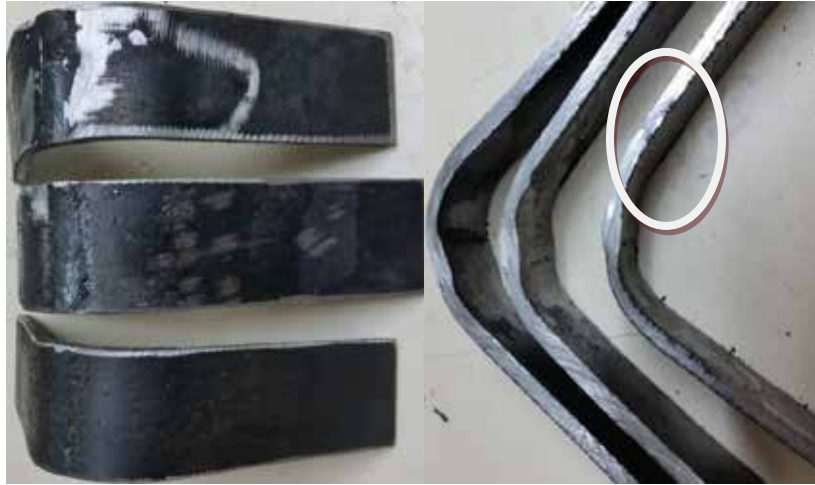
Doblado de la probeta soldada con electrodo E-6013 a 120Amp.
